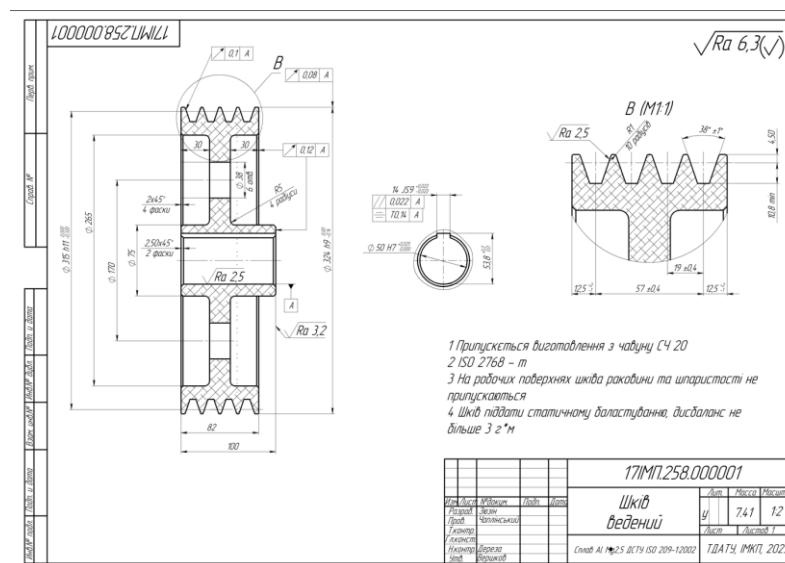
Робочій кресленник шківів клинопасової передачі
